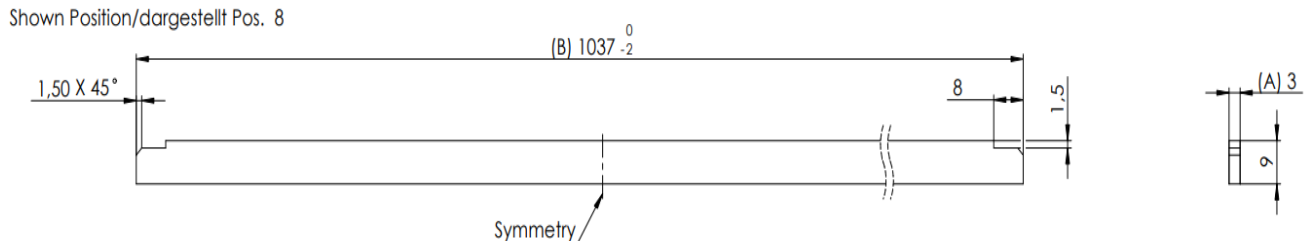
Кресленики повздовжньої смуги решітки
